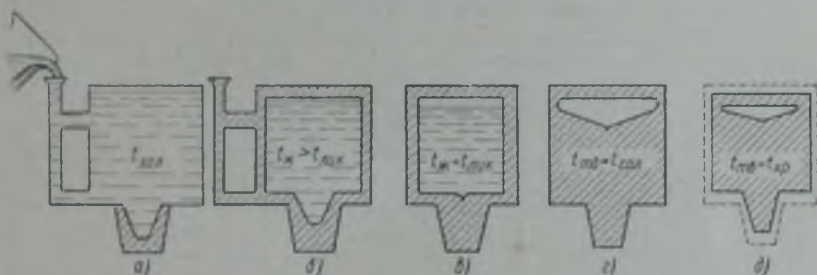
Схема образования усадочной раковины в фасонной отливке
